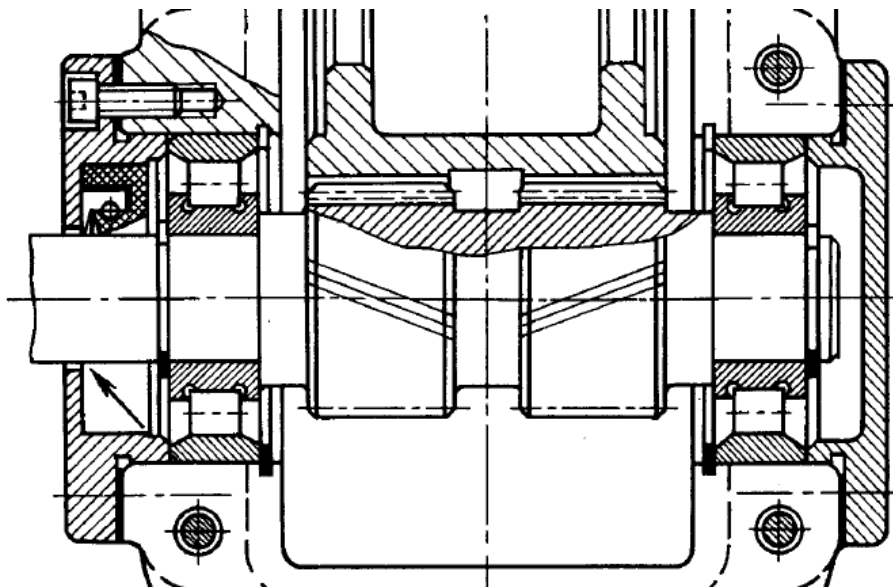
Схема установки подшипников «плавающий» вал.
